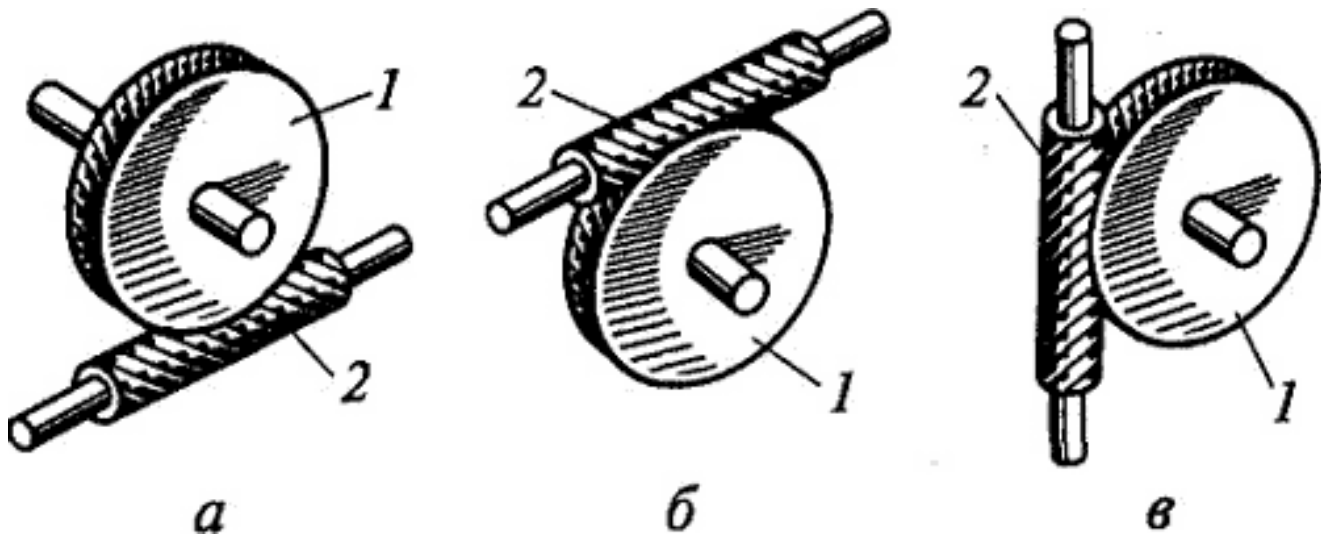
Схеми розташування черв'яка відносно колеса:
